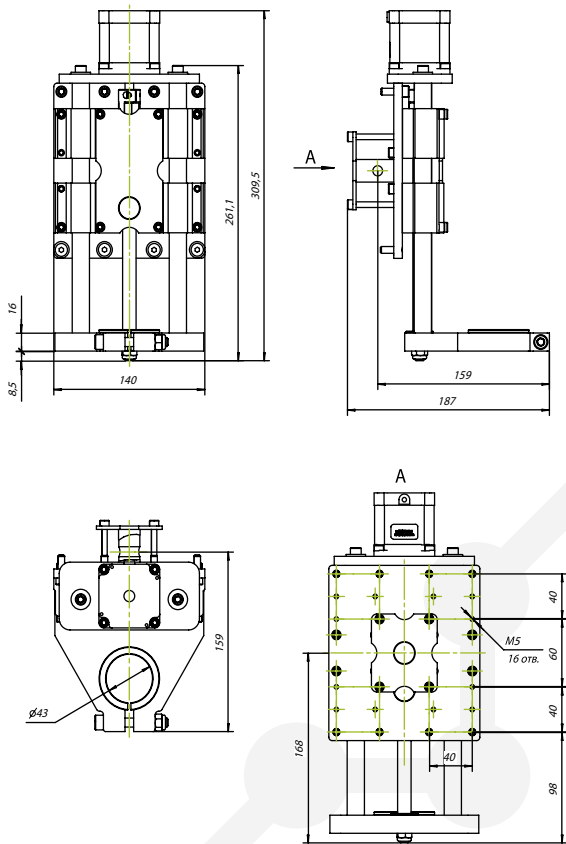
Габаритный чертеж модуля оси Z RY-Z089-RA4L
